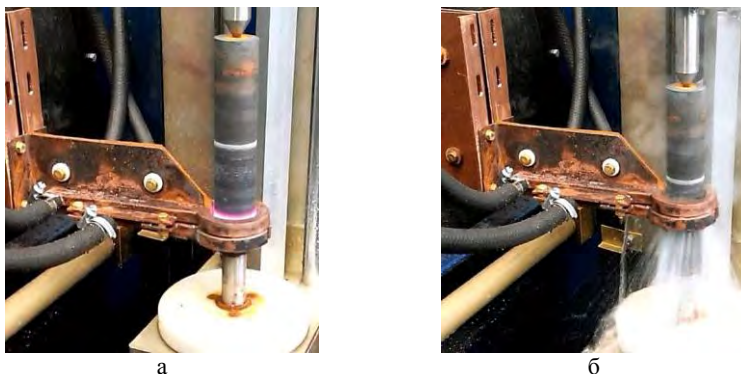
Индуктора для установки ФТИ-40/10-50
